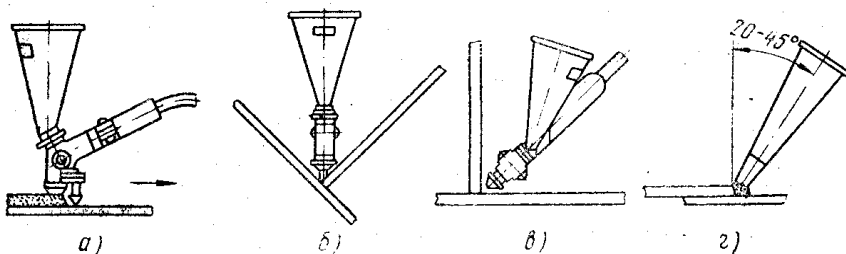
Схема полуавтоматической сварки под флюсом:
